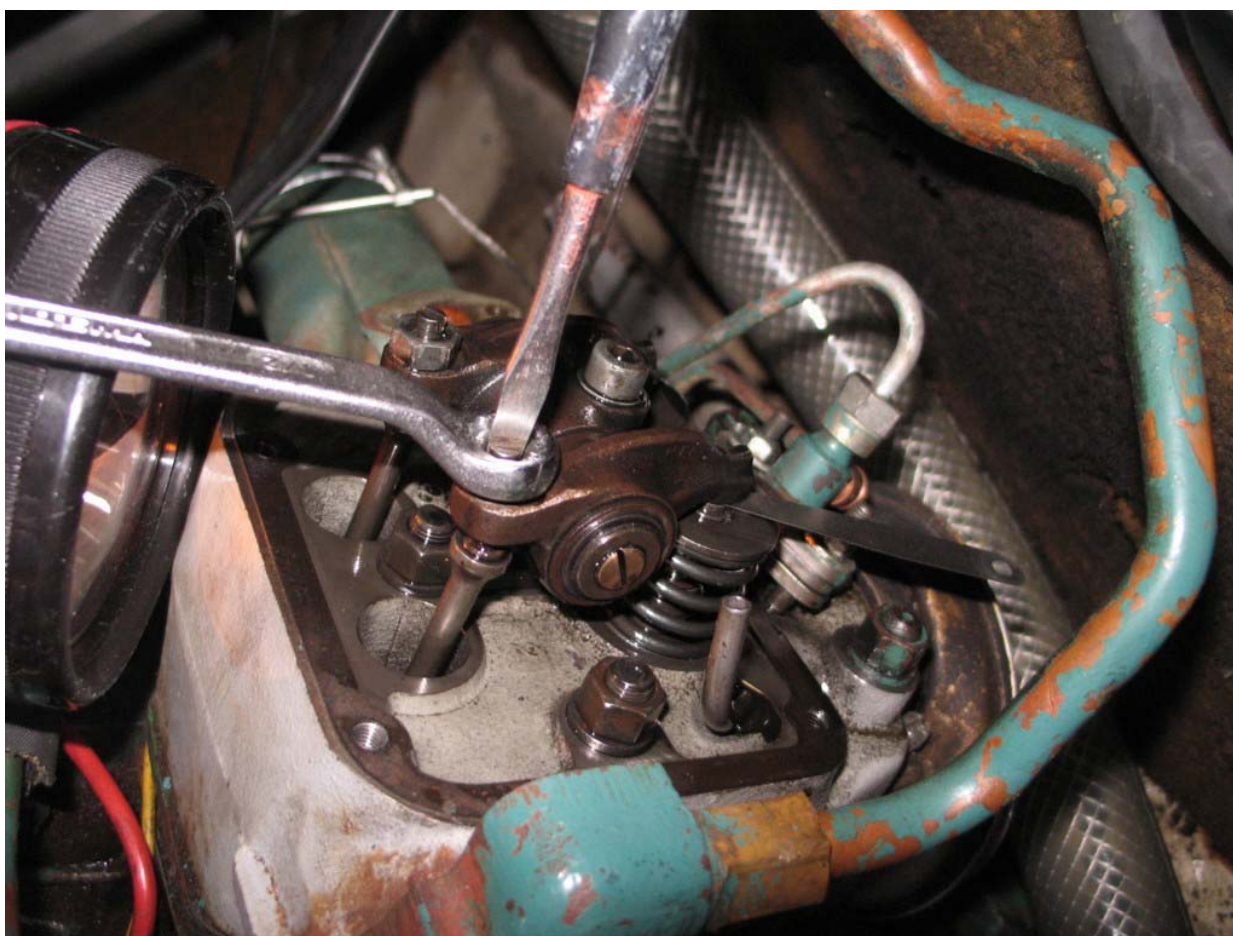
Ventiljustering. Jag brukar använda 13mm ringnyckel då ½" som gör det självboken säger inte passar,, skruvmejsel och bladmått. På bilden är det insugningsventilen som justeras till 0,3 mm, bladmåttet sitter på plats.
